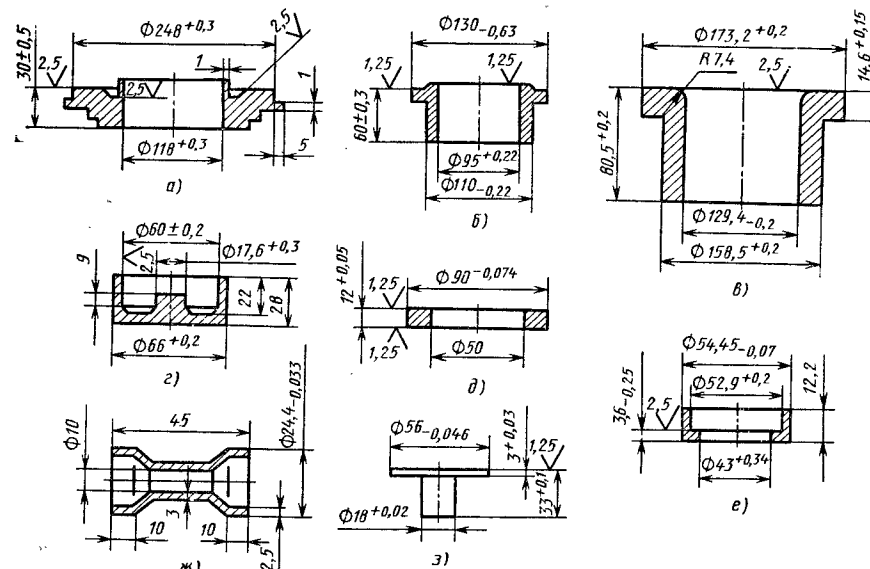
Примеры деталей, изготовленных торцовой раскаткой:
